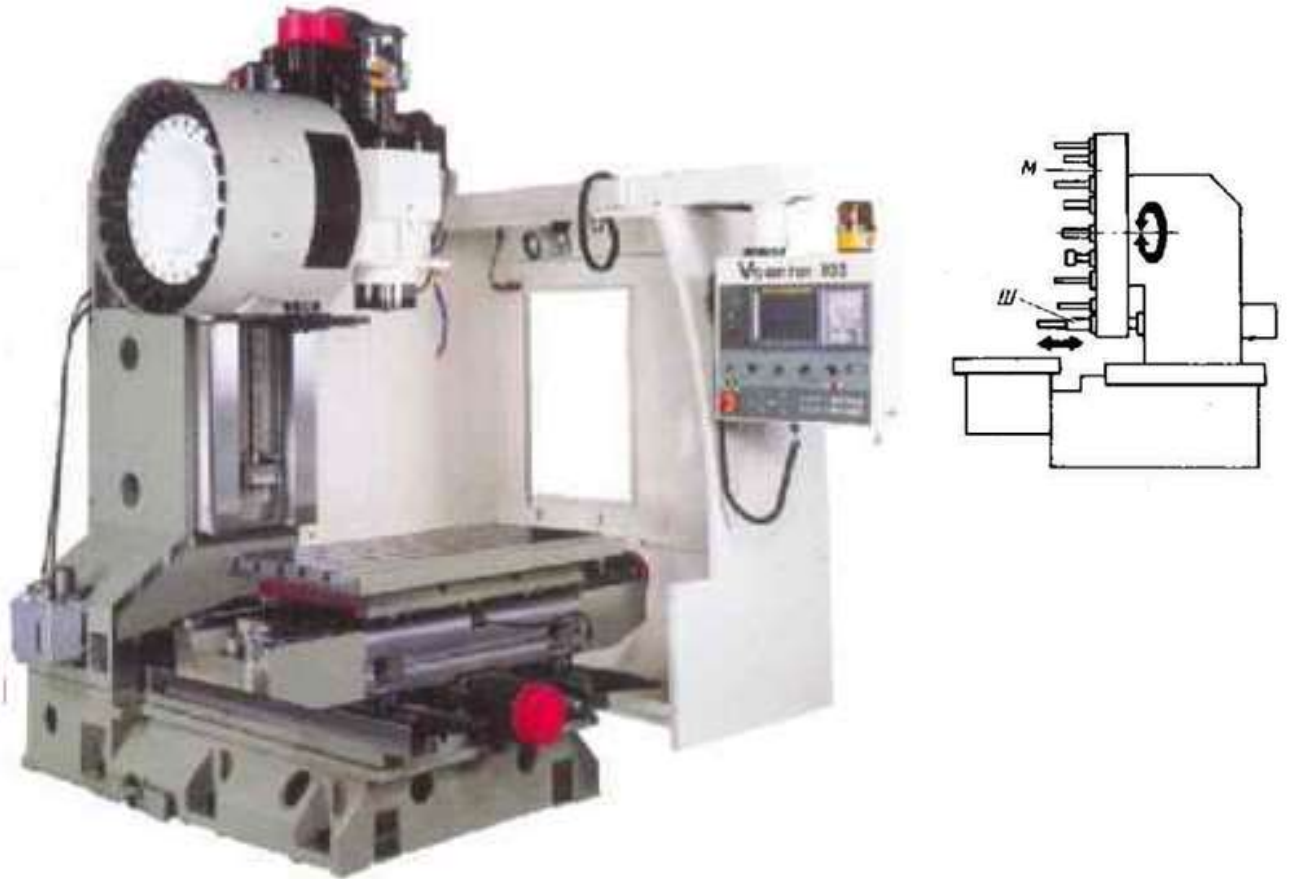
Інструментальний дисковий магазин, встановлений на шпиндельній бабці.
